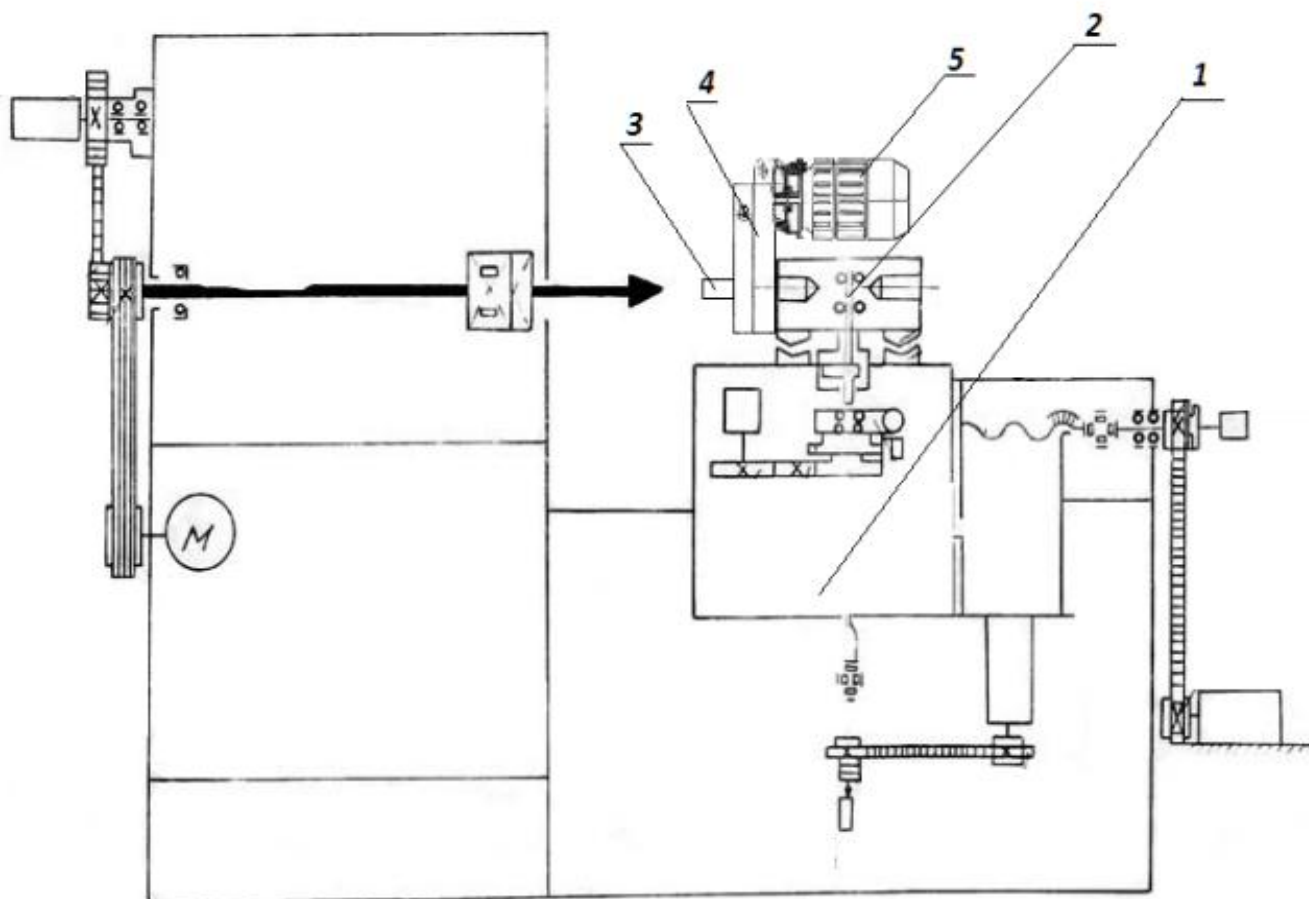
Токарный станок 1В340 с добавлением дополнительного шпинделя на резцедержателе для фрезеровки. (1 - станок 1В340, 2 - резцедержатель, 3 шпиндель фрезерной установки, 4 - редуктор, 5 — двигатель шпинделя)
